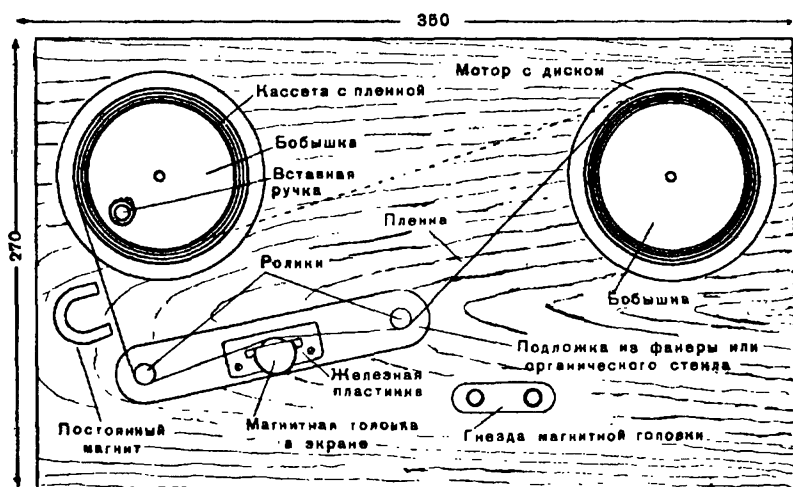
Общий вид лентопротяжного механизма звукозаписывающего аппарата.
